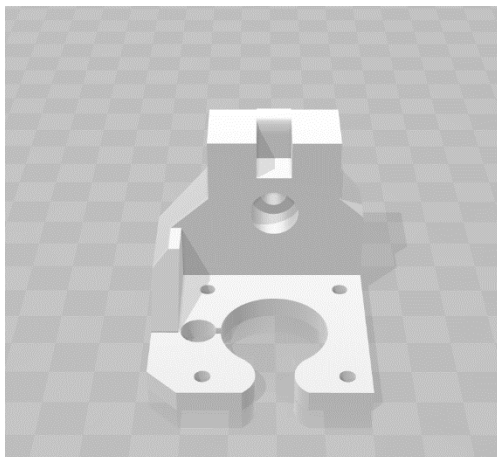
Uchycení motoru horní levé Autor: David Trcka
